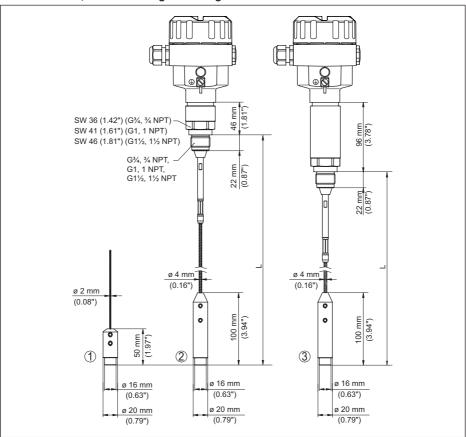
NivoGuide 8100, Gewindeausführung mit Straffgewicht (alle Straffgewichte mit Gewinde M8 für Ringschraube)
